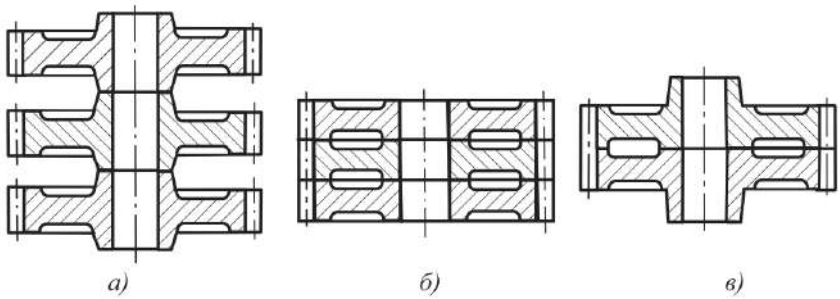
Підвищення жорсткості заготовки зубчастого колеса під час обробки шляхом зміни форми маточини
